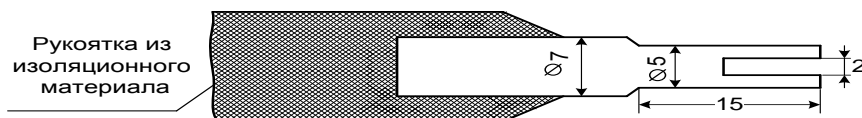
Приспособление для регулировки контактных пружин автопереключателя
